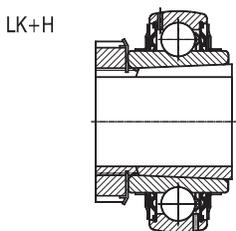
Регулируемые шариковые подшипники с закрепительными втулками -LK+H
